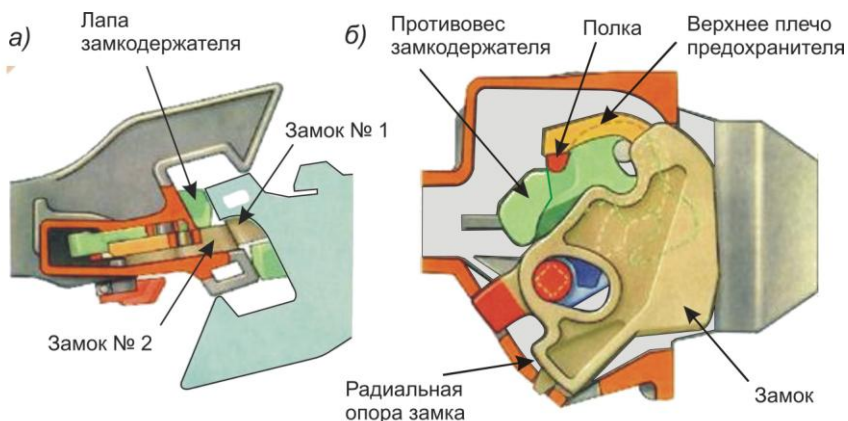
Положения деталей механизма сцепления автосцепок в начале сцепления (начало перемещения замка внутрь корпуса):
